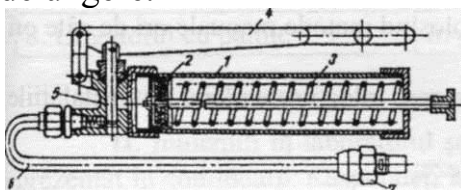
Pompa manuală pentru uns: 1 - corpul pompei; 2 - piston; 3 - arc de comprimare; 4 - manivelă; 5 - pistonas; 6 - furtun elastic; 7 - racord.
